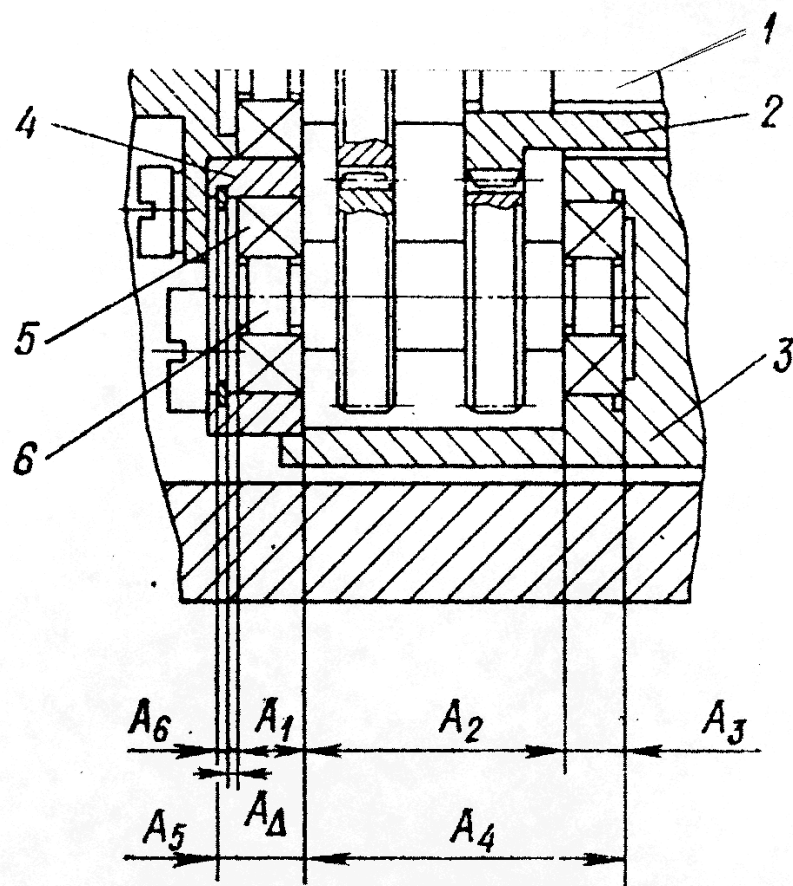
Узел подшипникового соединения: 1 – вал; 2 – колесо; 3- корпус; 4 – крышка; 5 – подшипник; 6 – ось
